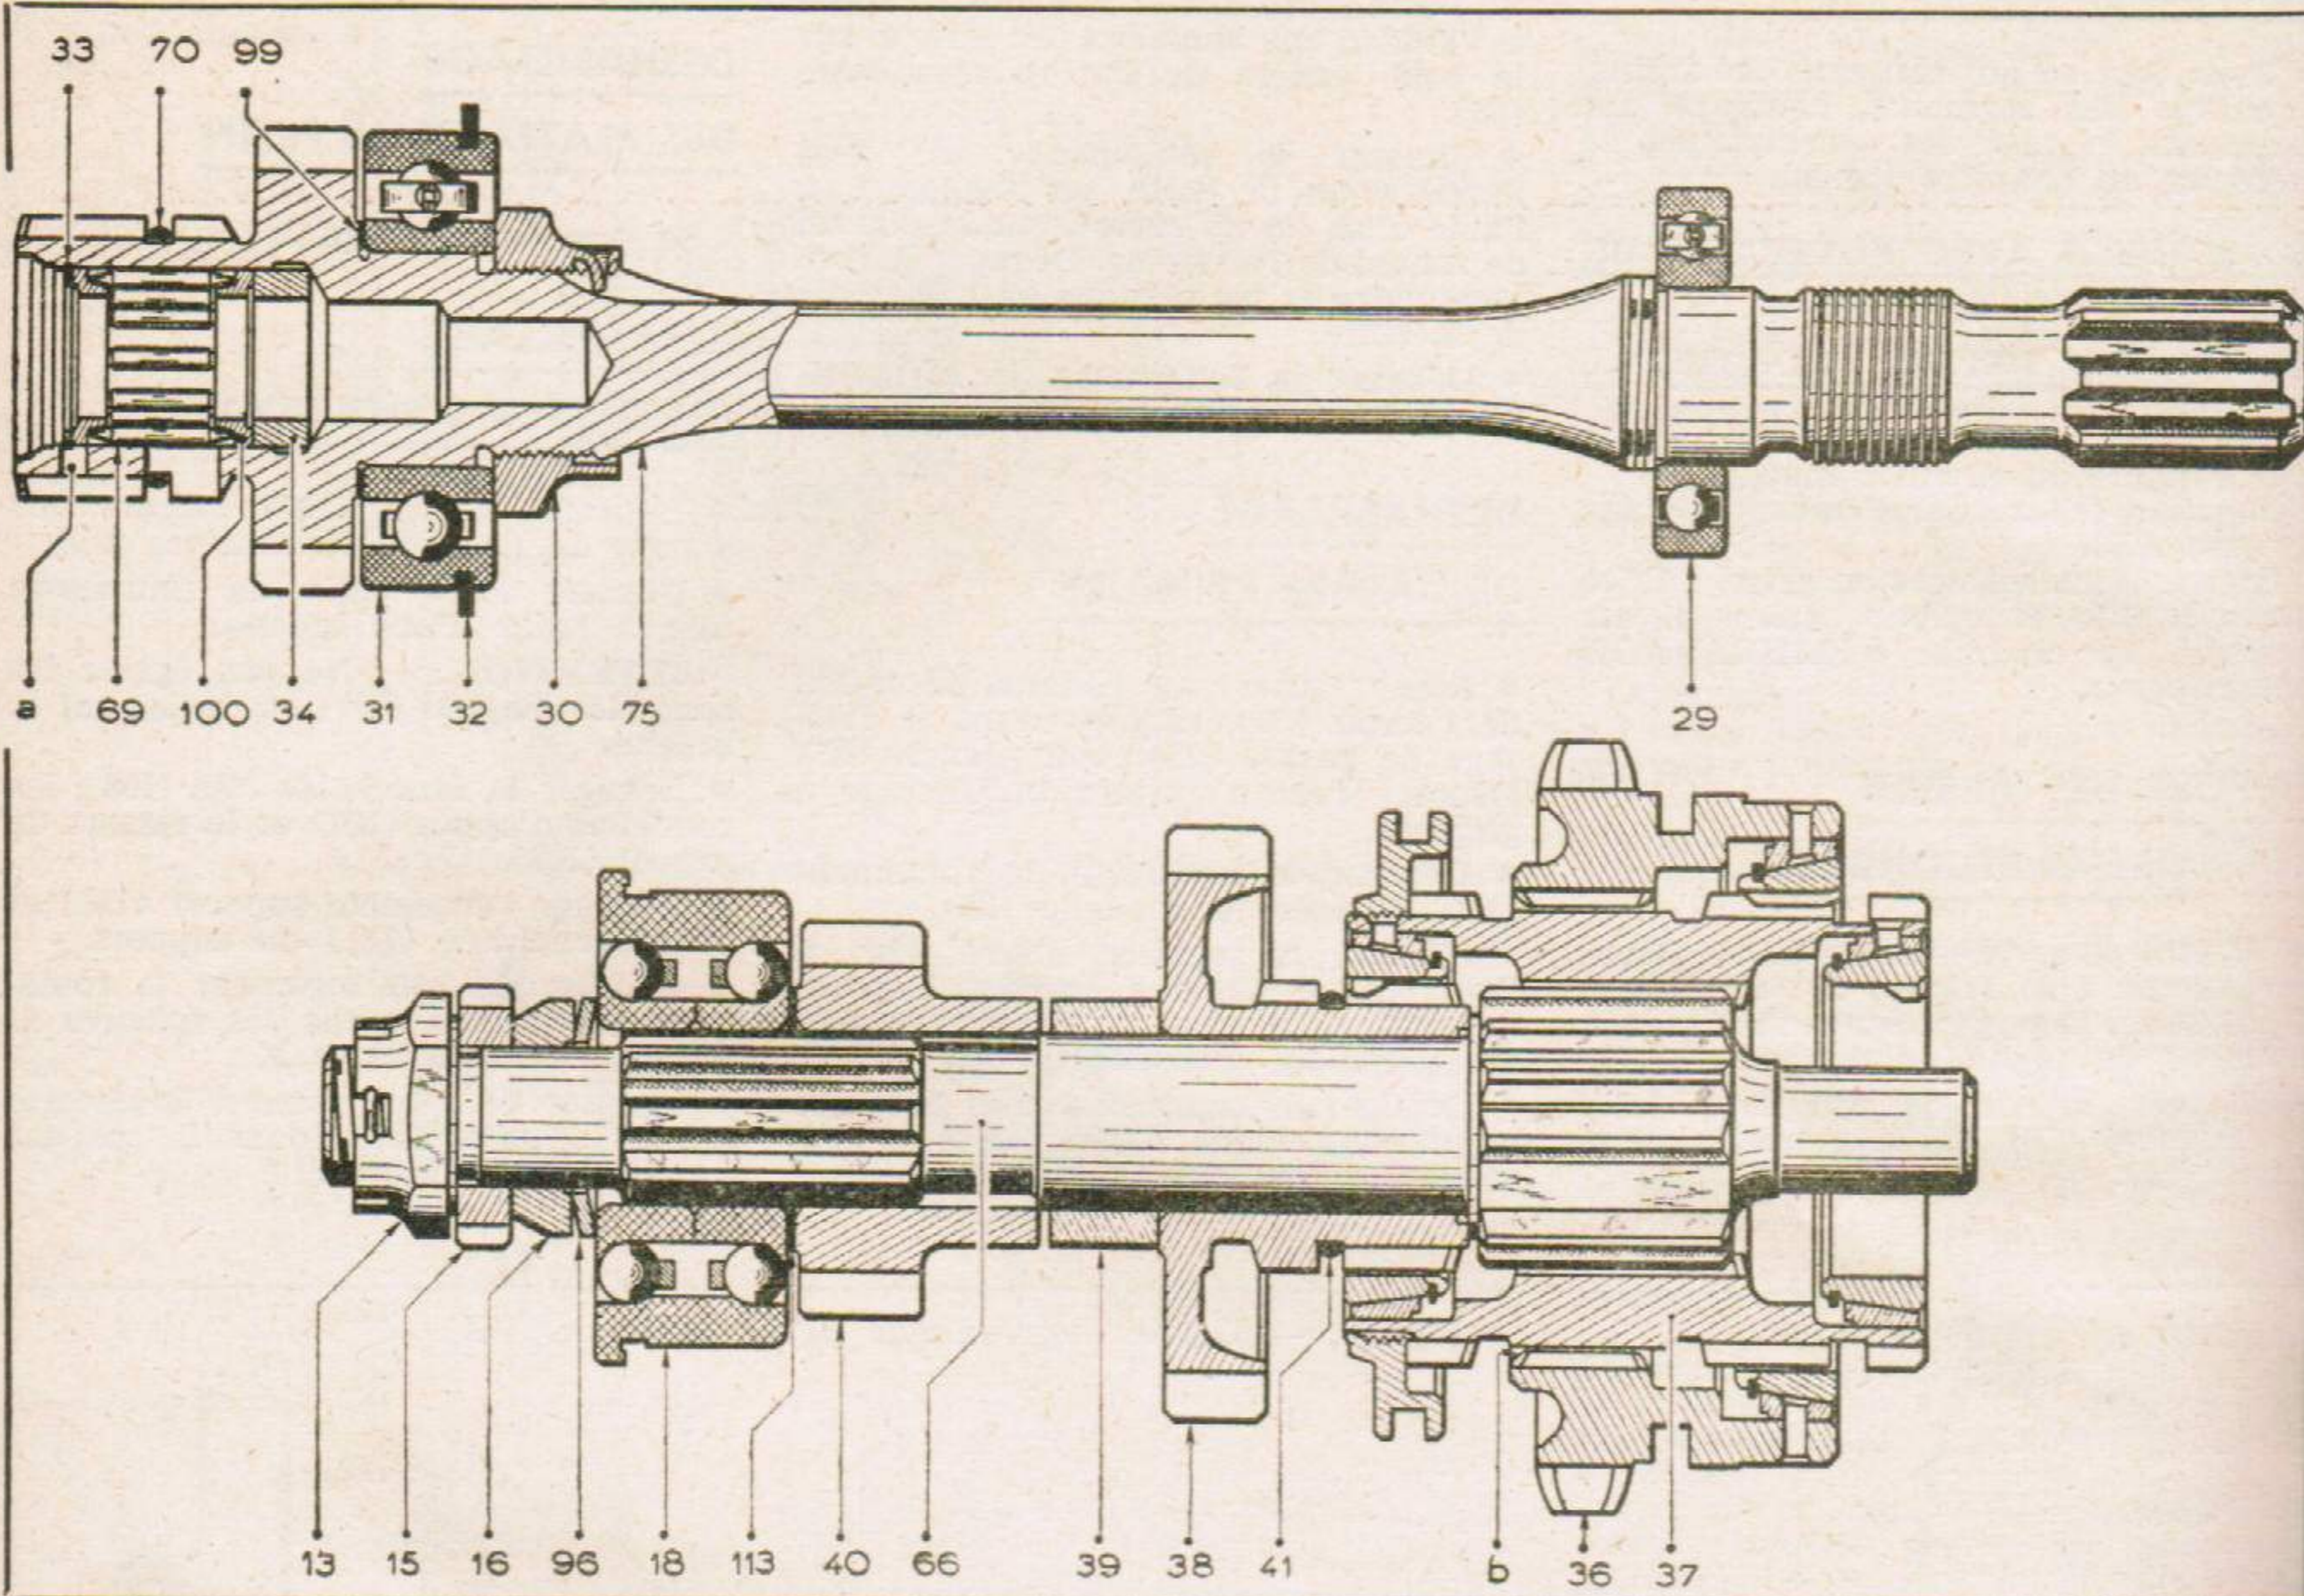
Coupe longitudinale de la boîte sur AZ
